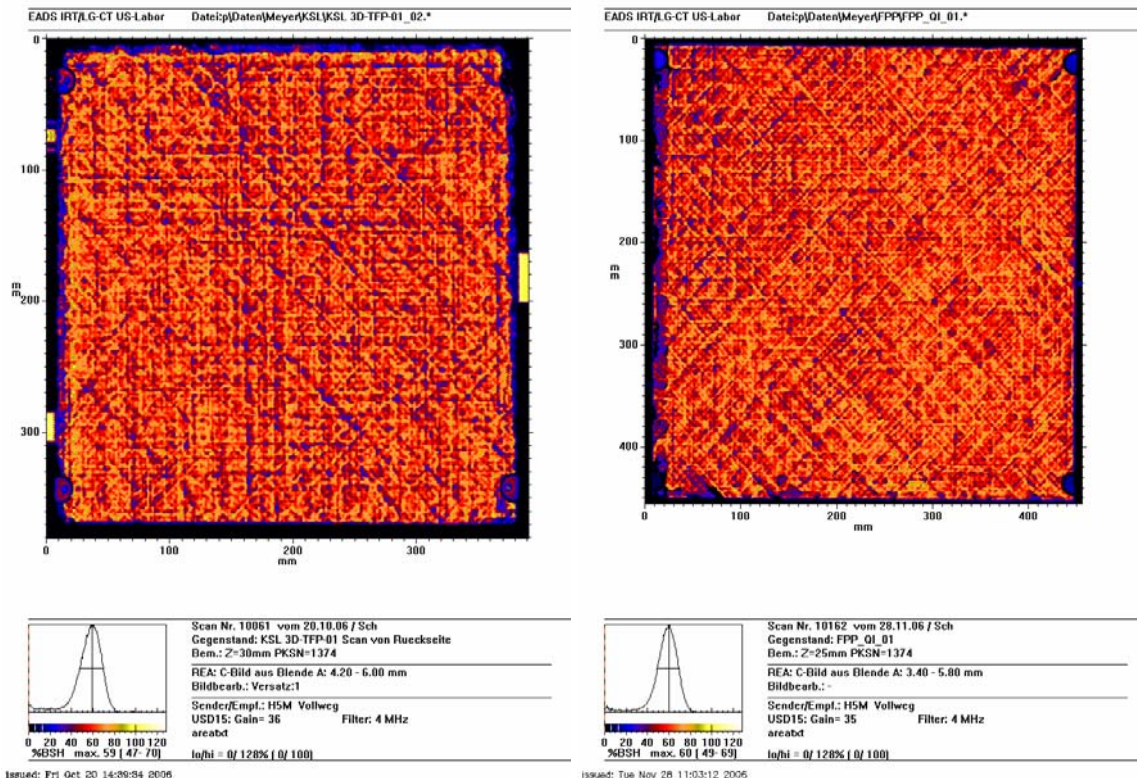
Ultraschall-Prüfprotokolle der 3D-TFP-Platte (links) und der FPP-Platte (rechts)
